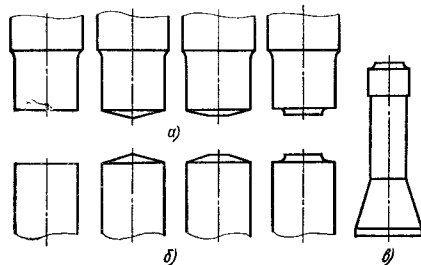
Схемы конструктивного оформления пуансонов и выталкивателей:
